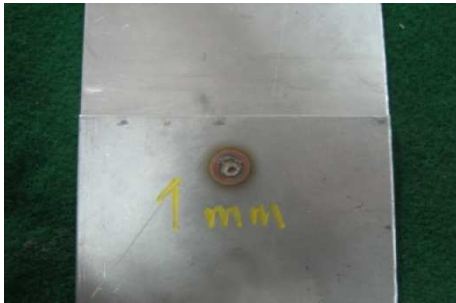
3. Punto de soldadura en la probeta de 1 mm.
